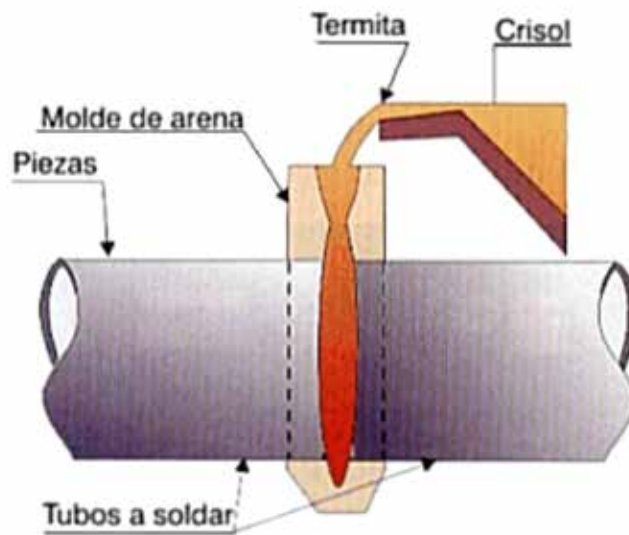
Soldadura con termita o aluminotérmica.
